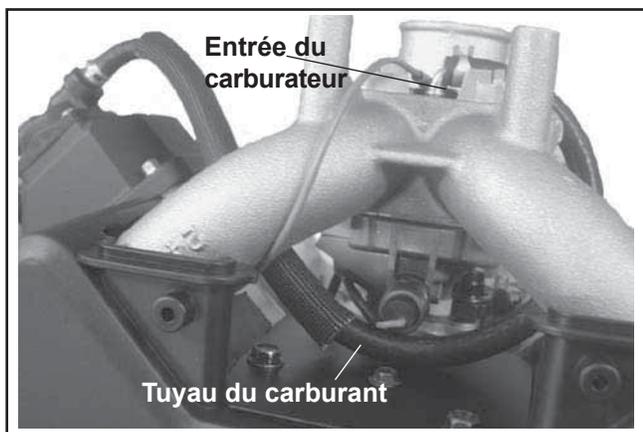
Détails du tuyau du carburant et du tuyau d'évent.
